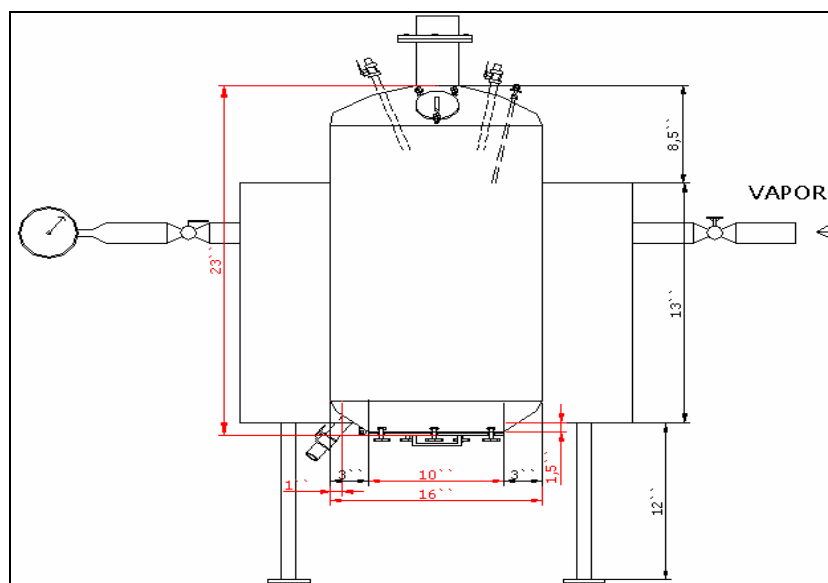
Vista frontal del diseño entregado al soldador para su modificación.
